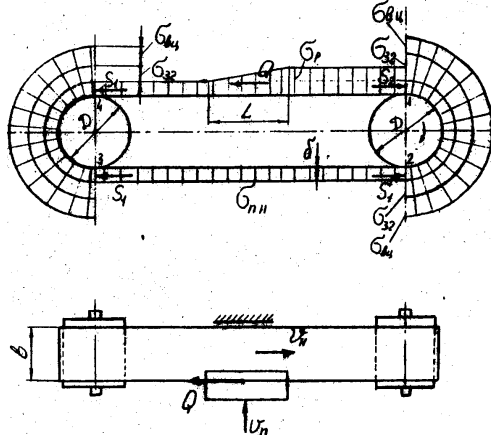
Розрахункова схема механізму стрічкового ножа
